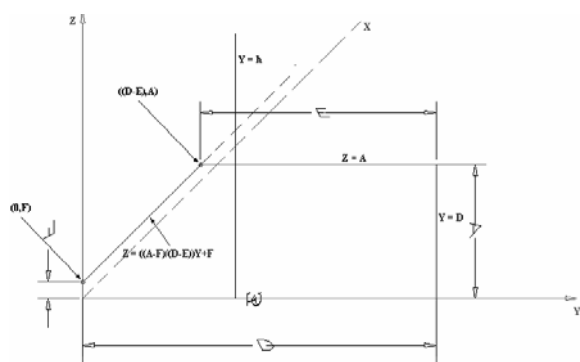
Construcción geométrica de la vista transversal del tanque 2
